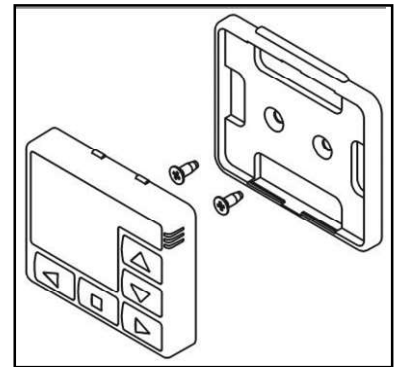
Installation des Bedienfelds PU-27 mit einer Halterung.
